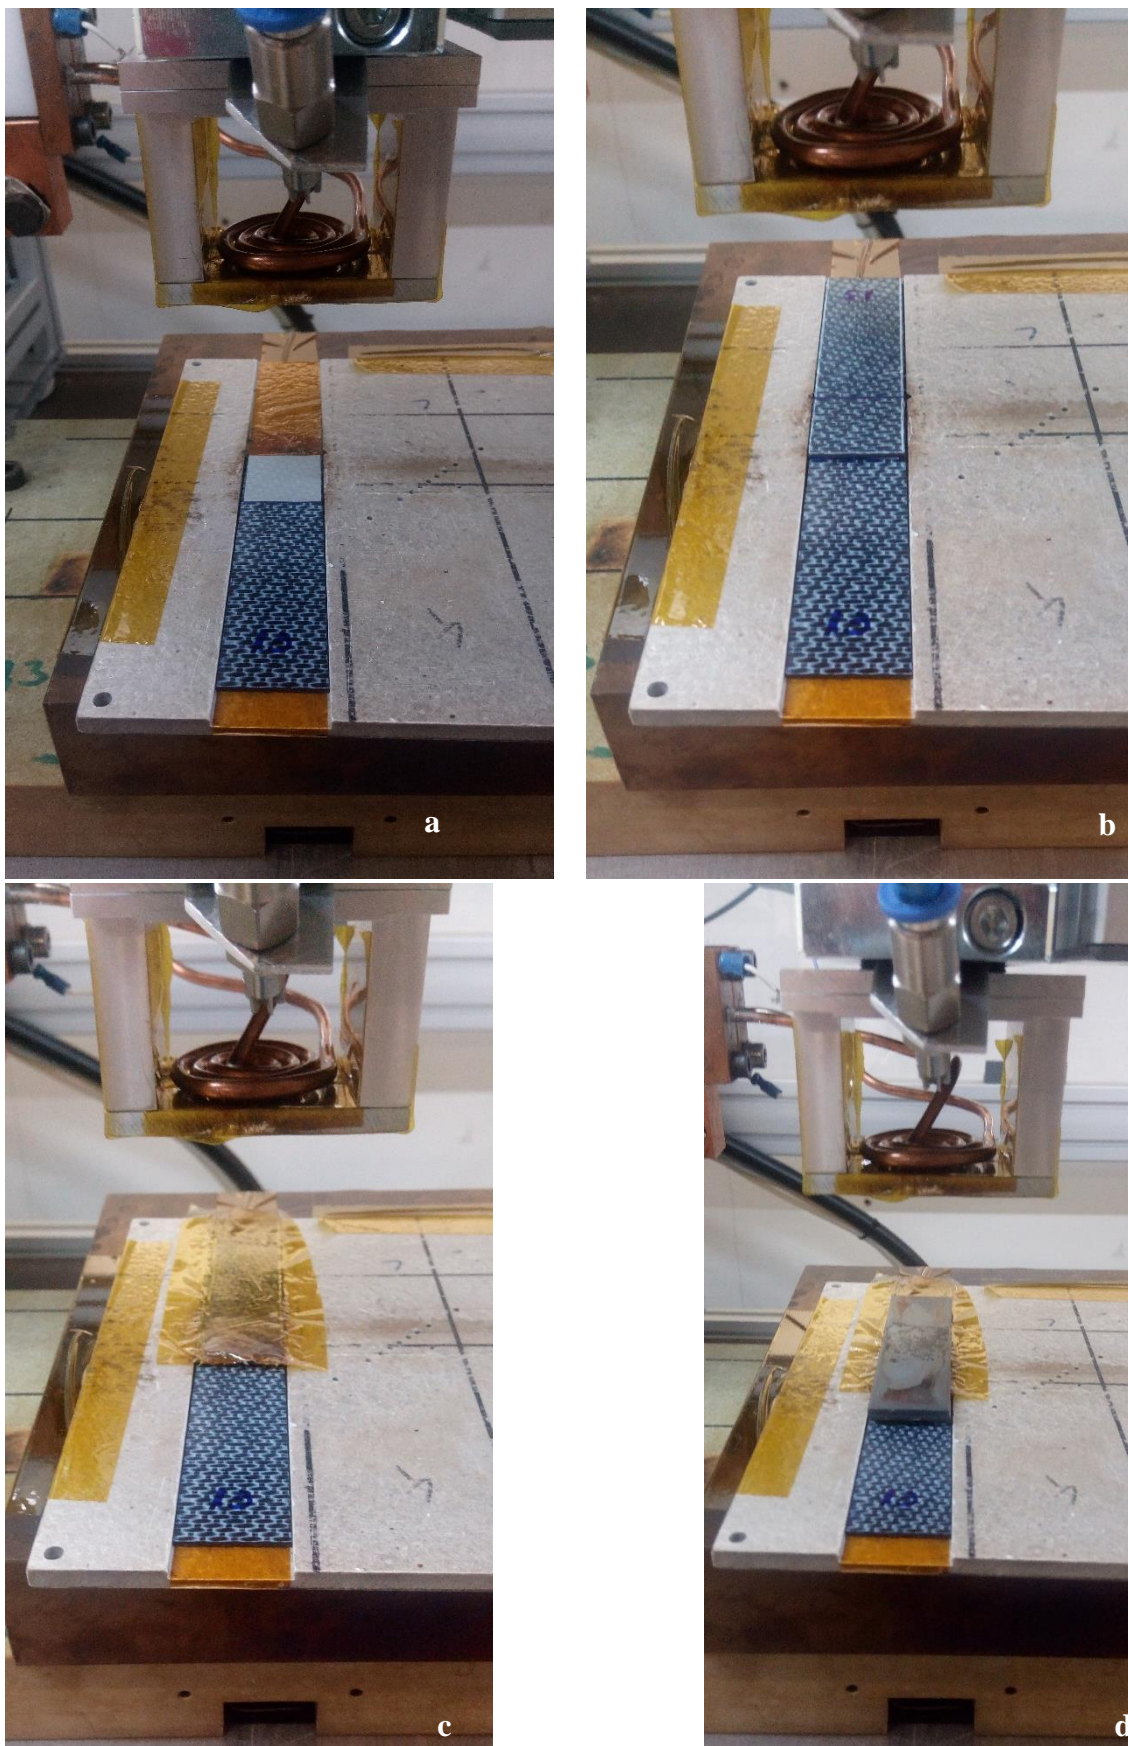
Soldadora pronta para a soldagem por indução.
